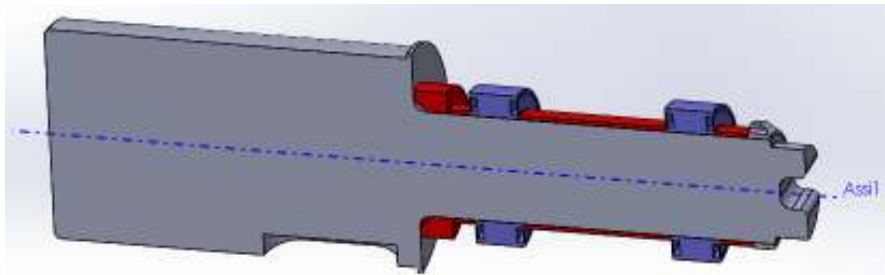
Vista assonometrica e in sezione dell'albero interno
